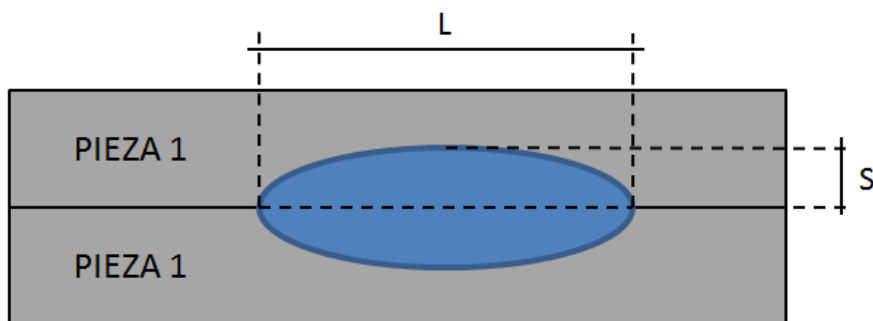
Dimensiones de control en un punto de soldadura.
